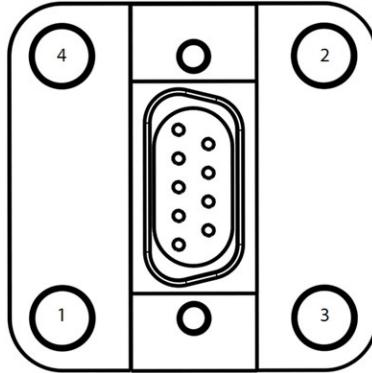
Desmontaje del pasamuros del sensor del cojinete (se muestra la parte trasera izquierda)
